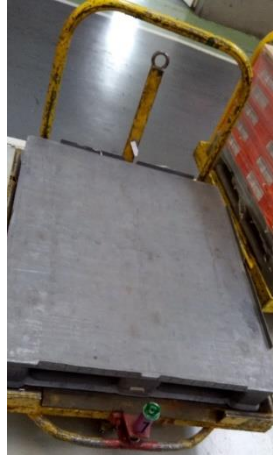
9 Carro vacío puesto de montaje [Foto interior Renault]
